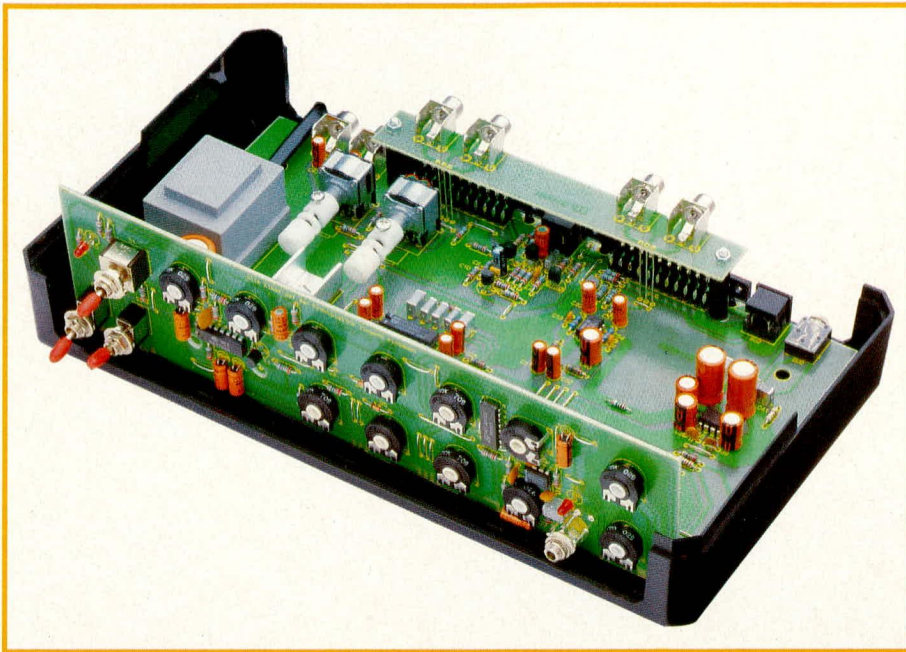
Innensicht des VDM 7000 vor Aufsetzen der oberen Halbschale. Die Montage erfolgt mit einem Minimum an Einzelteilen.
